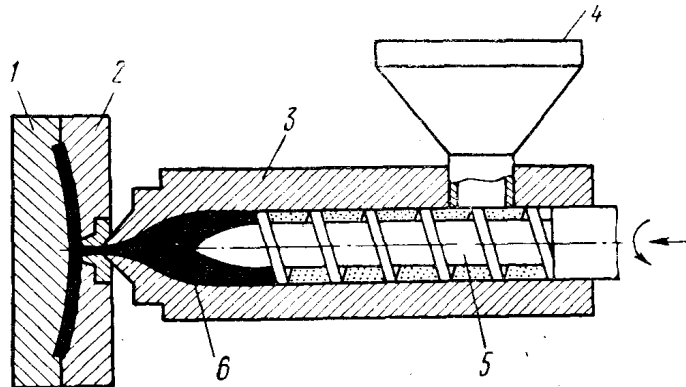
Схема дії ливарної машини з черв'ячною пластикацією:
